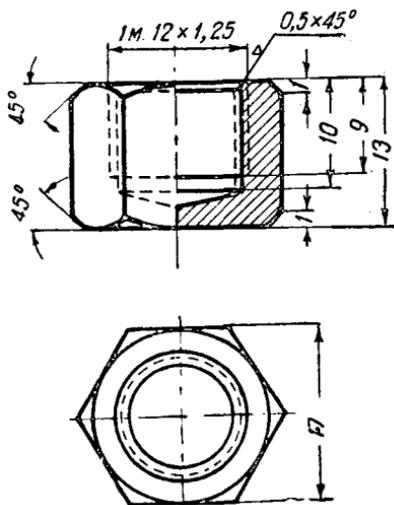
Дет. № 333. Гайка на корпус фильтра топлива и воды
